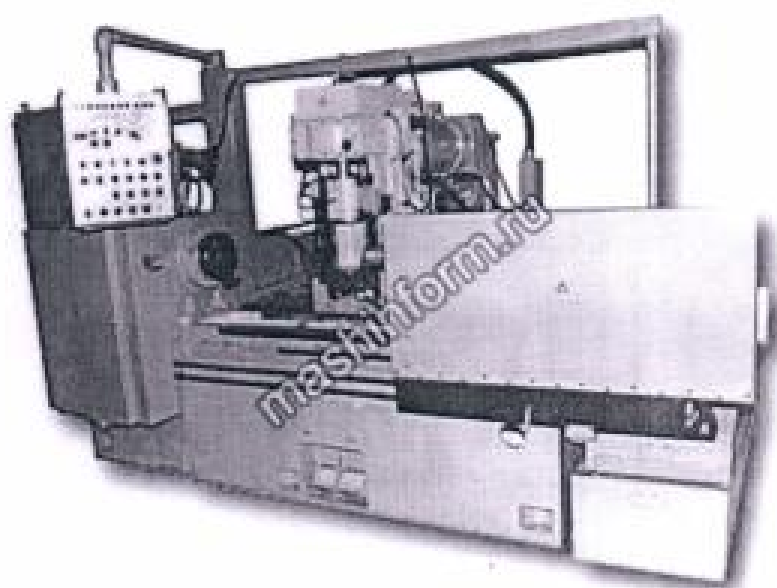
Загальний вигляд токарно-фрезерного верстата з ЧПУ ВЗ-729Ф4
